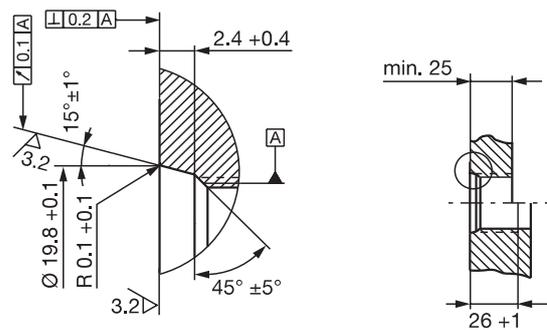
Einschraubloch M18x1.5 nach ISO 6149 O-Ring 15.4x2.1
